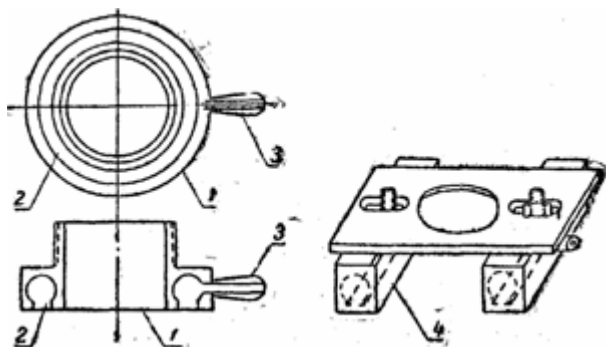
Приспособление для растягивания поверхности кожного покрова.
